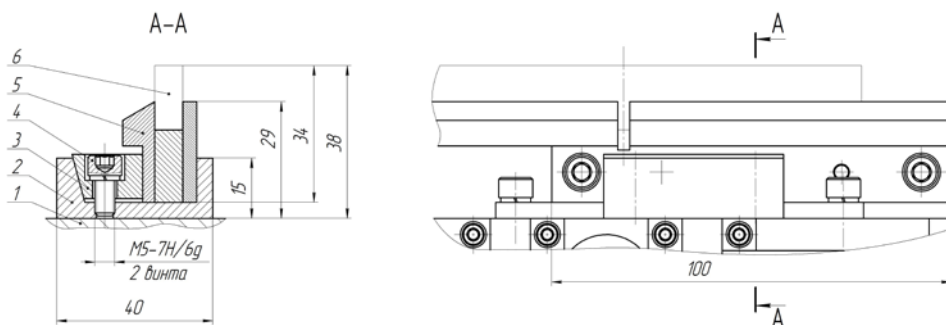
Конструктивная схема крепления приспособления клином: 1 – верхний стол;
